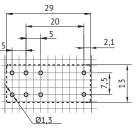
Установочные размеры для печатного монтажа для pene OptiRel G RP40-52 и OptiRel G RP40-61 с CO контактами
